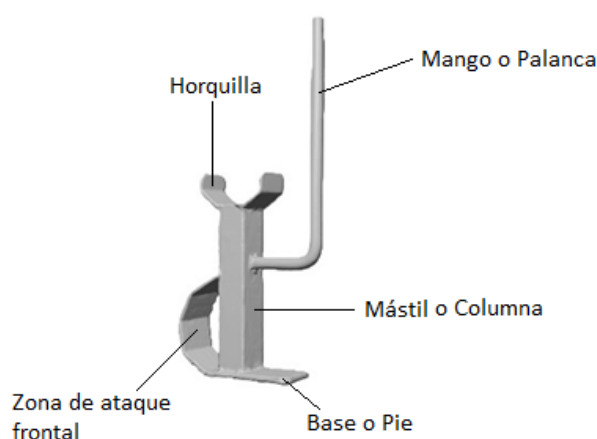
Vista en perspectiva del dispositivo elevador de barras con pesas de gimnasio
